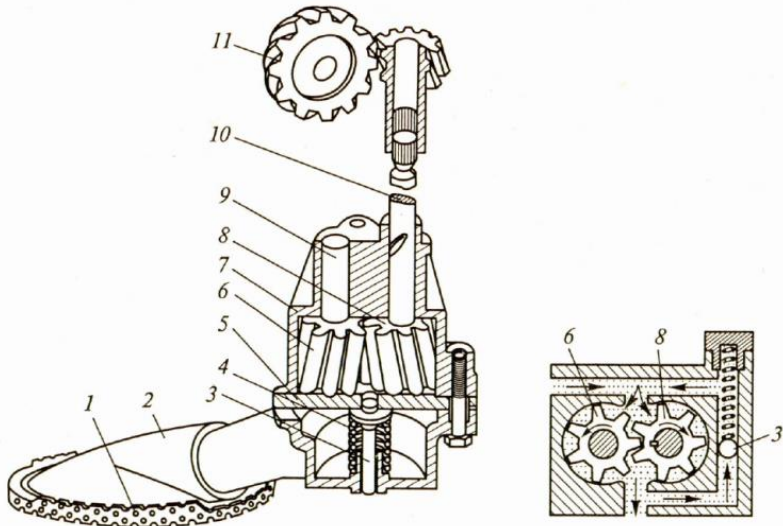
Схема та принцип дії шестеренчастого масляного насоса: 1 – фільтр маслозабірника; 2 – патрубок; 3 – редукційний клапан; 4 – пружина клапана; 5 – кришка; 6, 8 – шестерні; 7 – корпус; 9 – вісь; 10 – вал приводу; 11 – шестерня приводу
